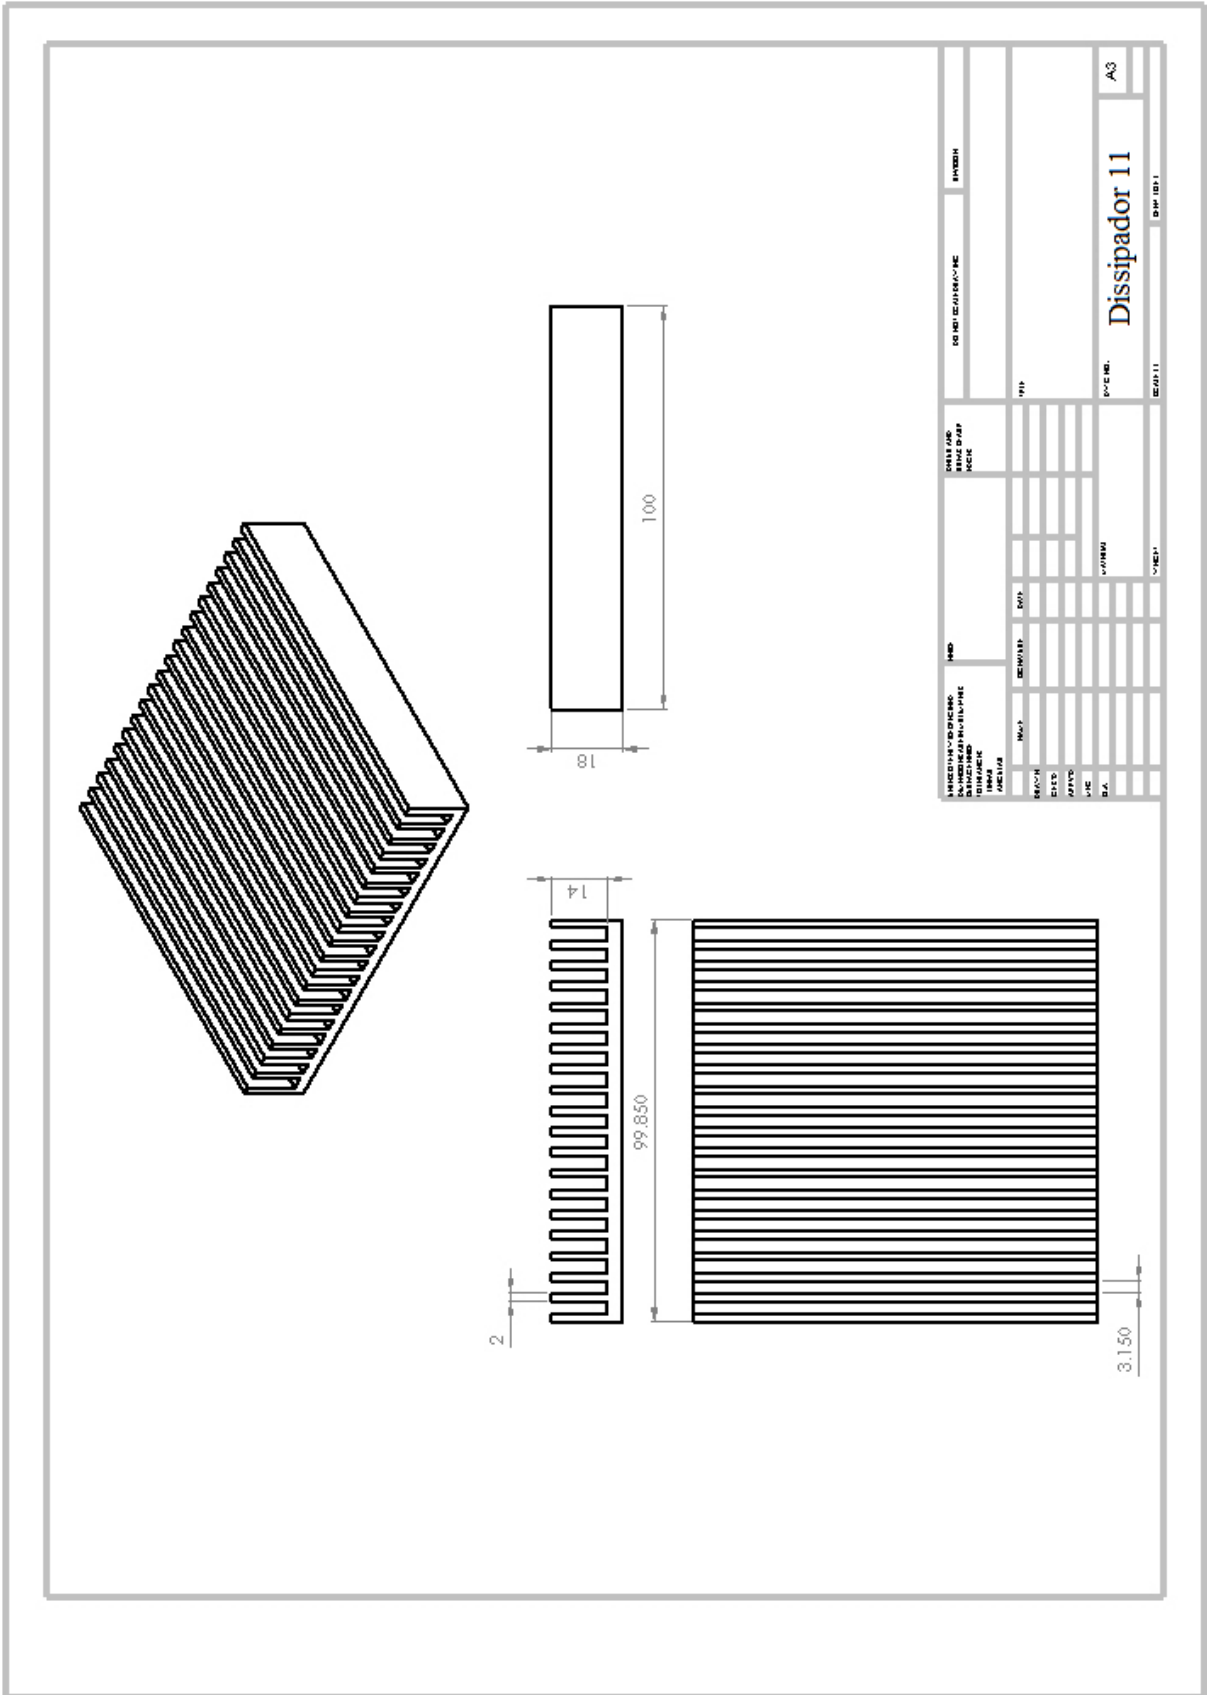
Desenho técnico utilizado para confecção do Dissipador 11.
